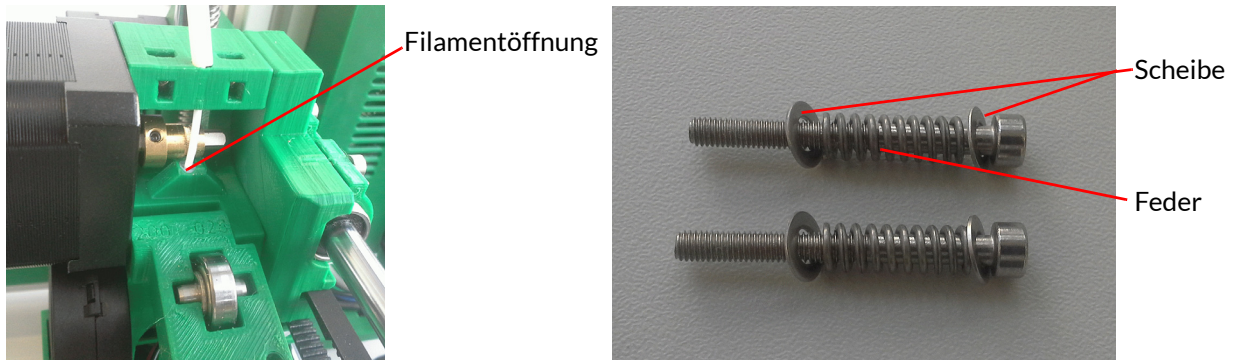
Extruder: Anpressrolle und Schrauben mit Andruckfeder
